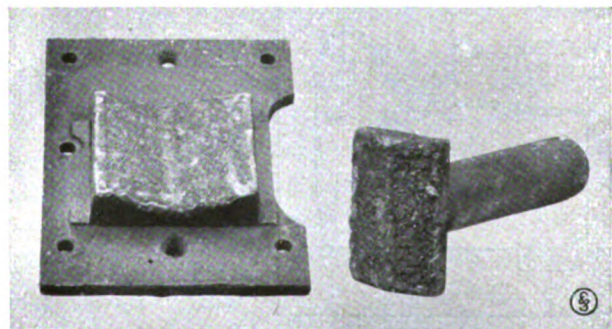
Durch Lichtbogenschweißung instand gesetzter Stoßpuffer.
